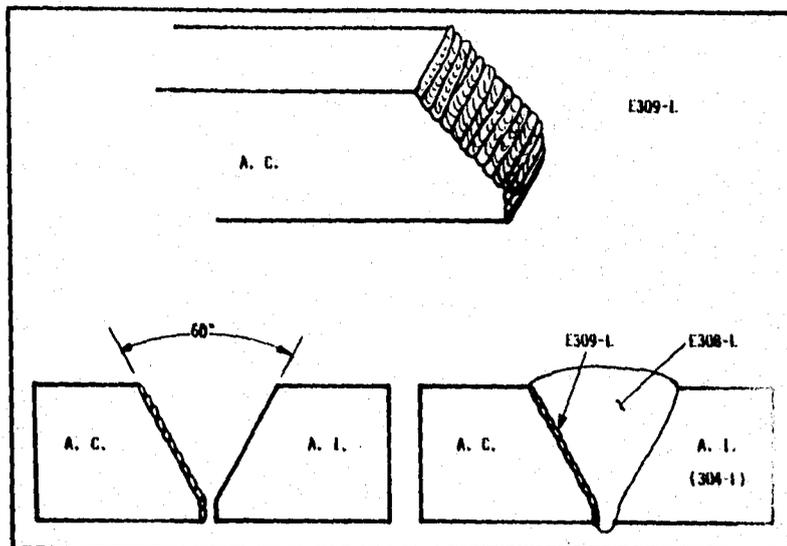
DESARROLLO DE SOLDADURA DE METALES DISIMILES.
